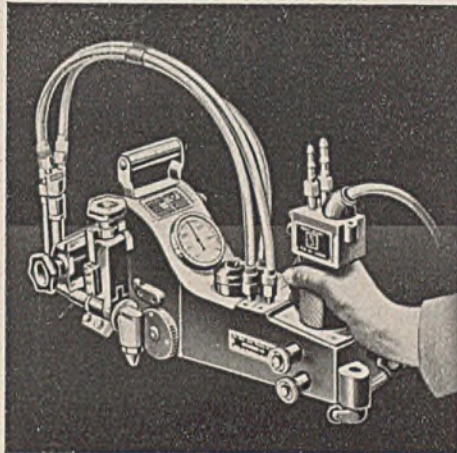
Gasschneidbrenner mit Vorschubmotor und Führung des Wagens von Hand von Messer & Co., G. m. b. H.
